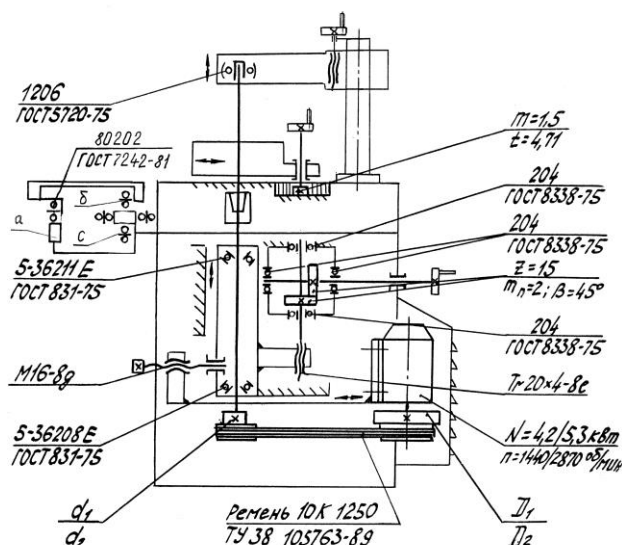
Схема совмещенная кинематическая и расположения подшипников.
